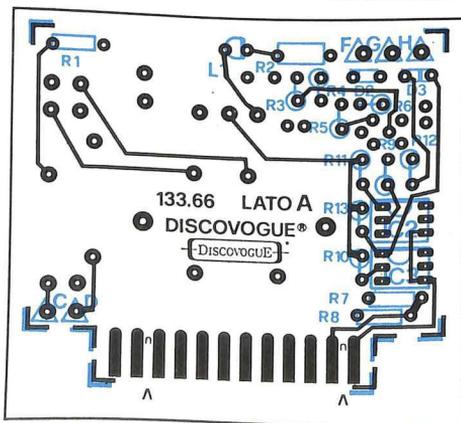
Pista conduttrice del lato A del circuito stampato principale con componenti montati.
